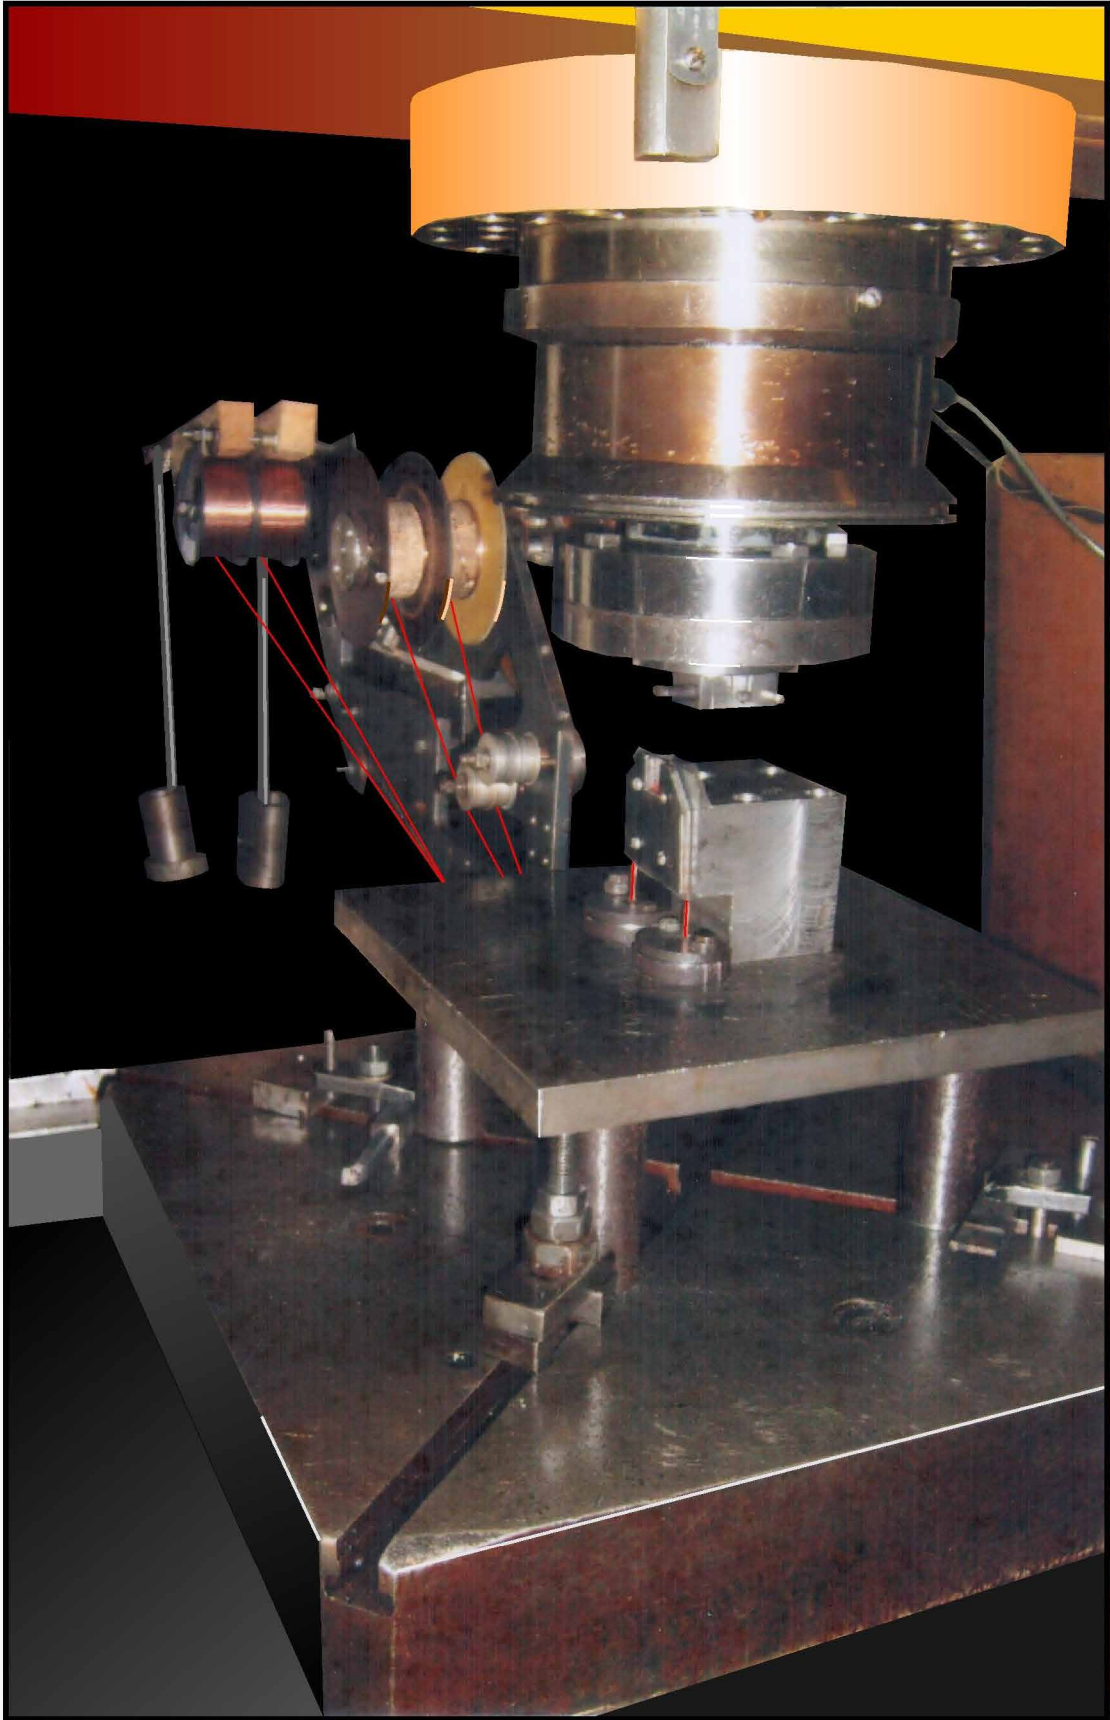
Експериментальний пристрій для електродугового різання металів дротовими електродами-інструментами з використанням зворотного прокачування органічного середовища (верстат "Дуга-8Г")
